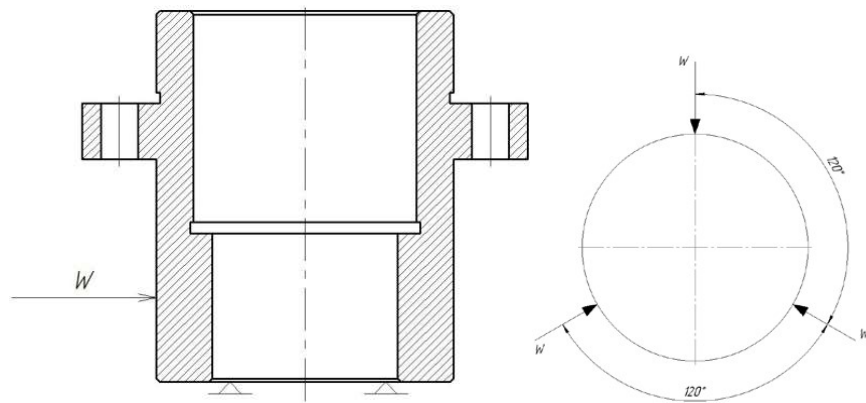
Принципова схема затиску заготовки у пристрої із зазначенням місць сили затиску
